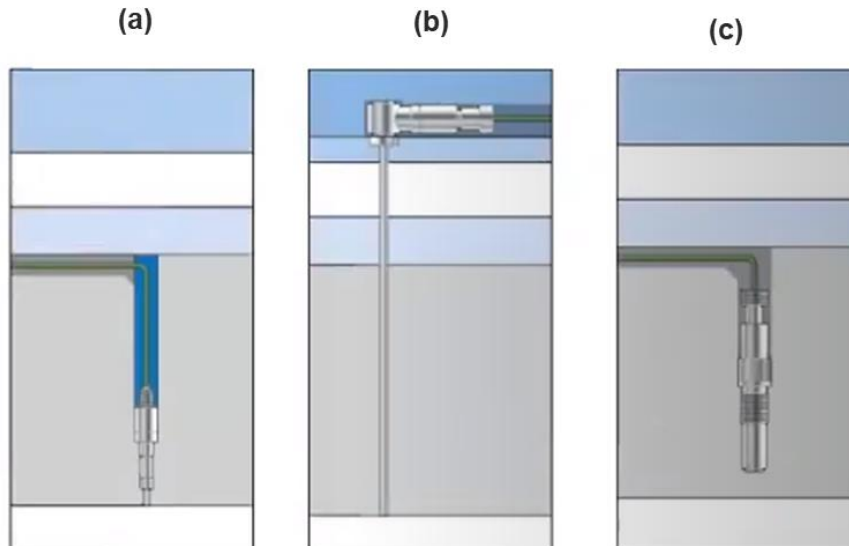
Sensores de medição de pressão: (a) medição direta, (b) medição indireta e (c) medição sem contacto [44].
